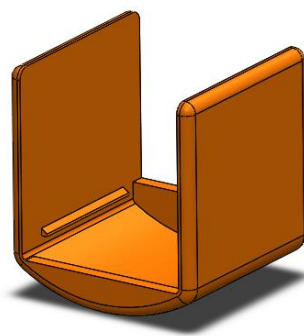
Общий вид литевой детали из ПКМ «Заглушка»
